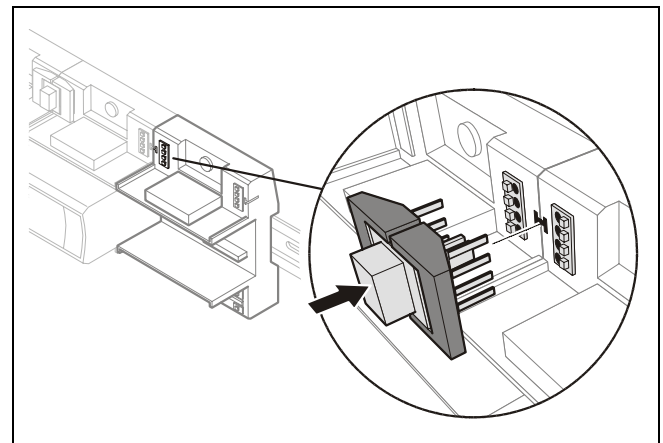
Verbinden der Klemmenblöcke mit dem Verbindungsstecker
